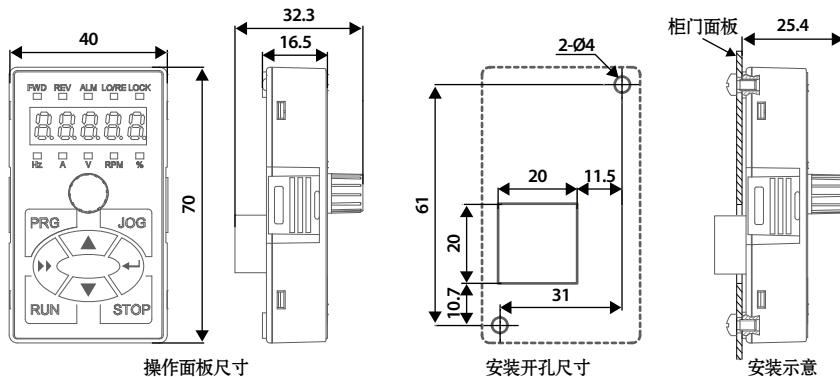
HD-LED-P-S 尺寸及开孔尺寸
